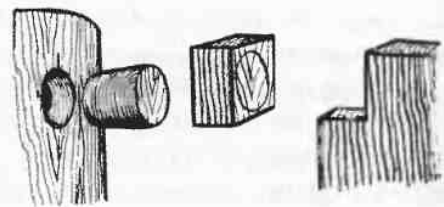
Заделка пробкой отверстия от сучка. Заготовка пробки
